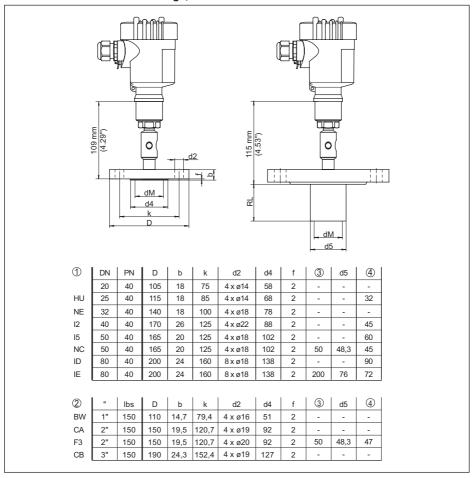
VEGABAR 81 - Conexão com flange, medidas em mm
